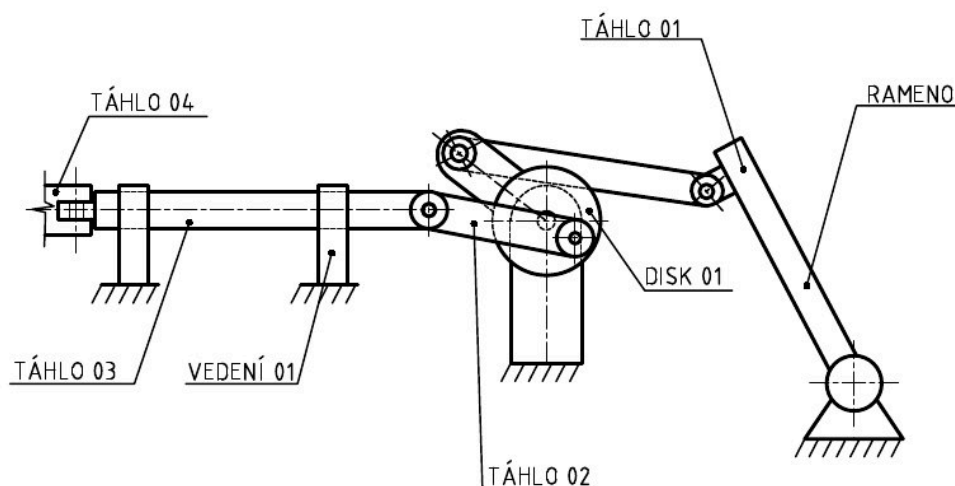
Schéma principu otvírání na straně hydraulického pístu – pohled z boku
